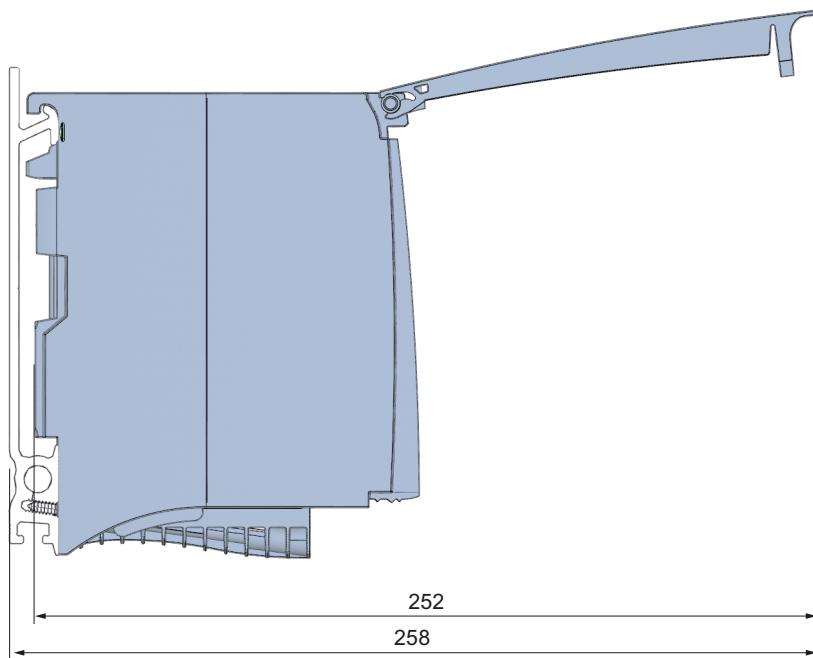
Габаритный чертеж блока питания PS 60W 24/48/60VDC, вид сбоку с открытой передней панелью
